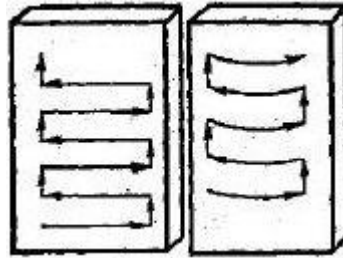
Схема движения электрода при выполнении широких валиков при сварке стыковых соединений в вертикальном положении
